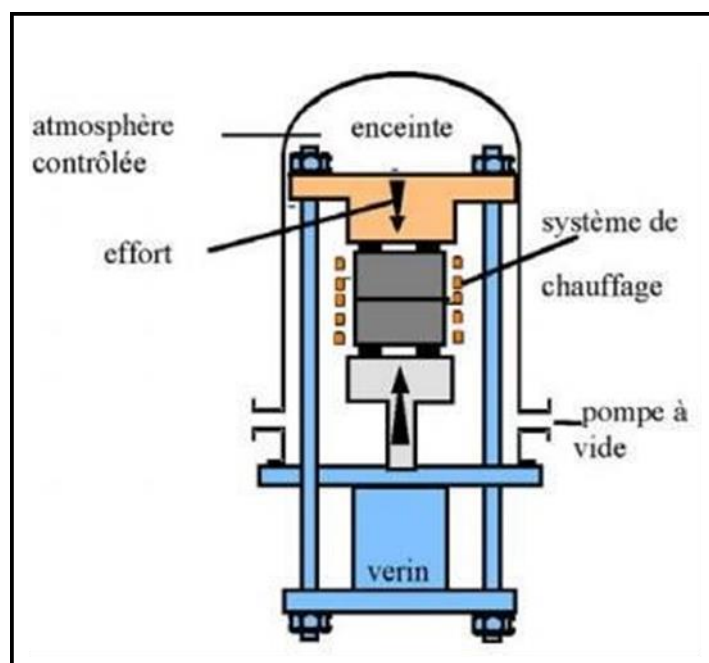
Schéma du principe de soudage par diffusion.
